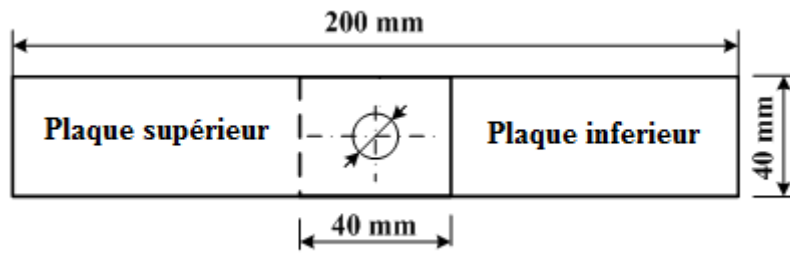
les dimensions des éprouvettes soudées par point
